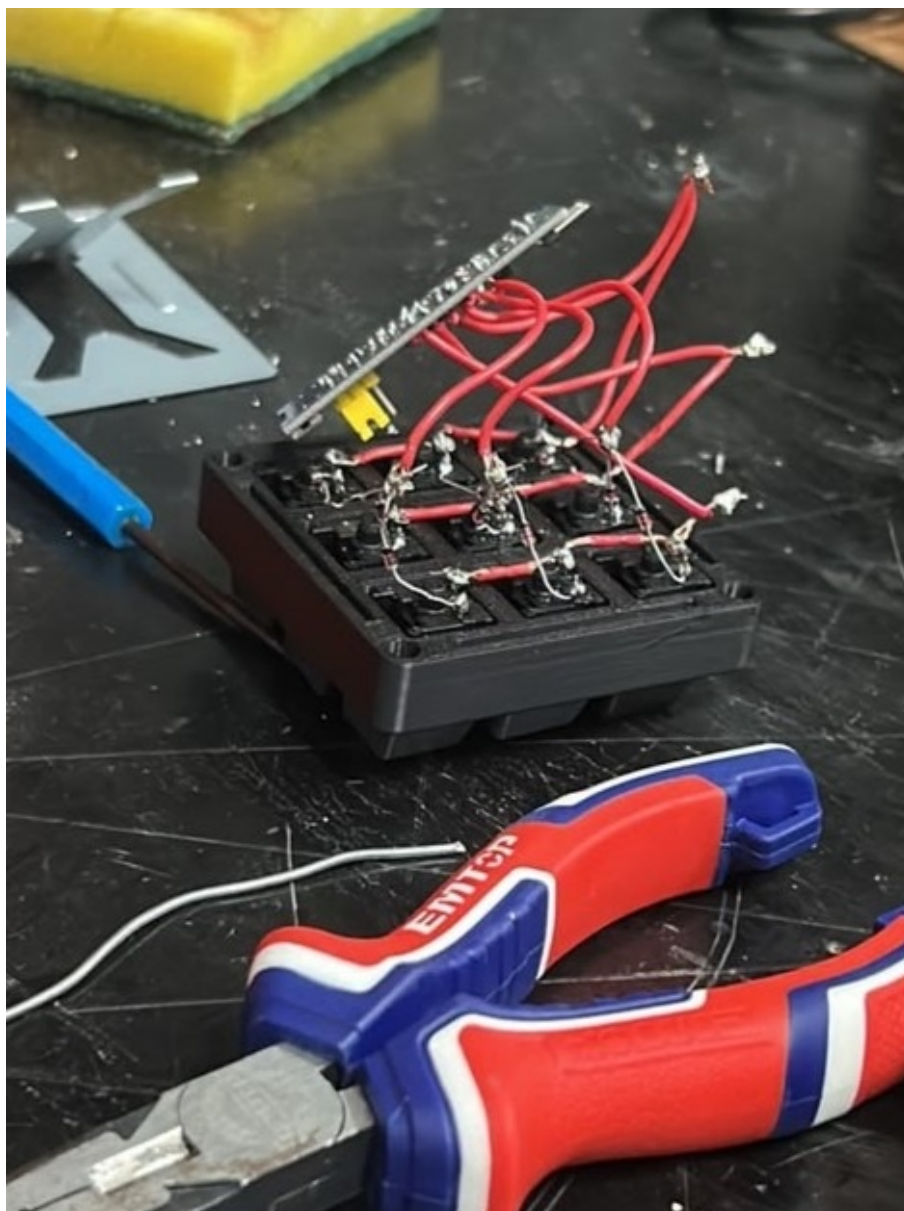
Processo de soldagem e montagem física dos switches mecânicos e diodos 1N4148.
